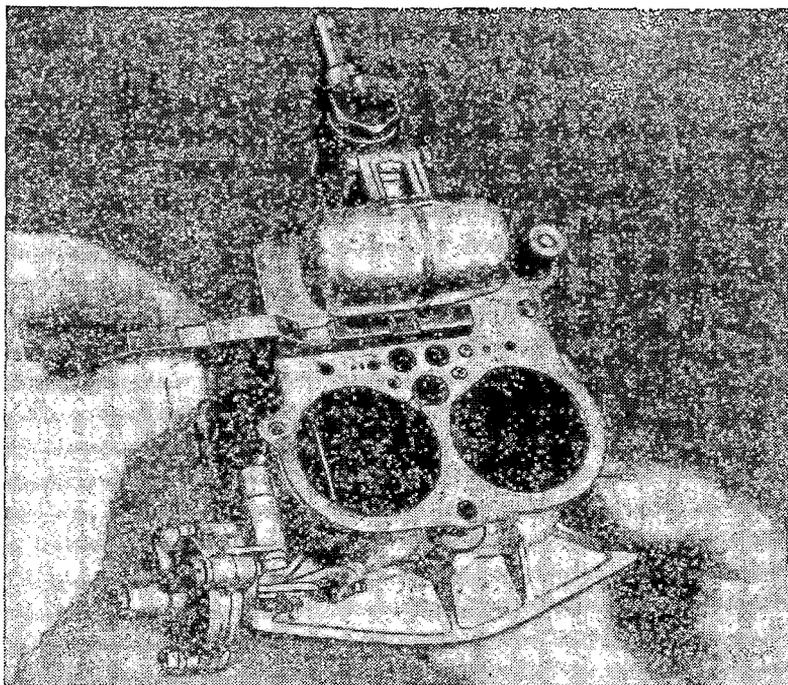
Проверка уровня топлива в поплавковой камере калибром 67.8151-9505
